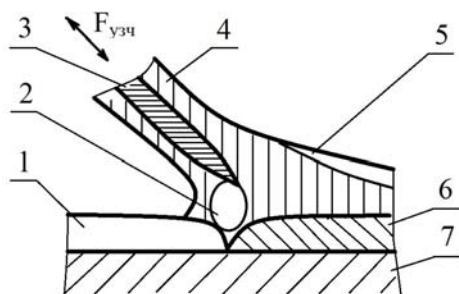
Схема ультразвуковой пайки и лужения
